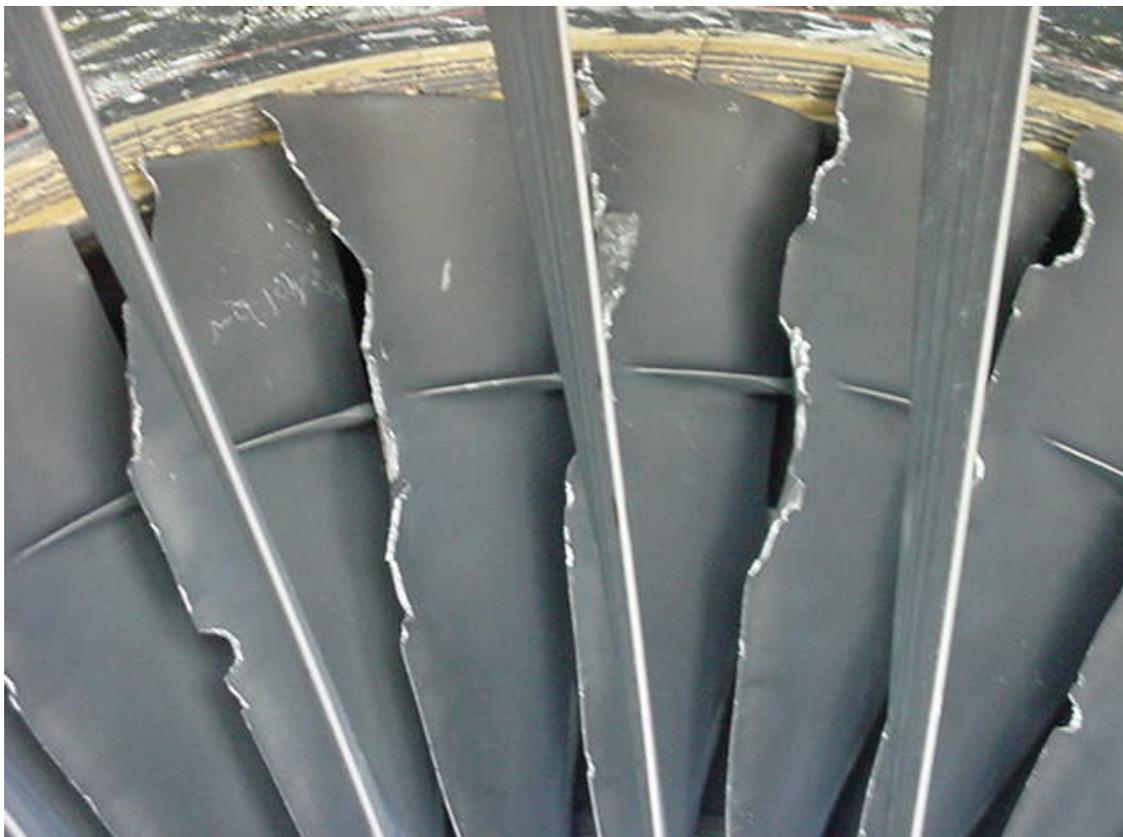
particolare danneggiamenti primo stadio rotatorio compressore motore sinistro.
